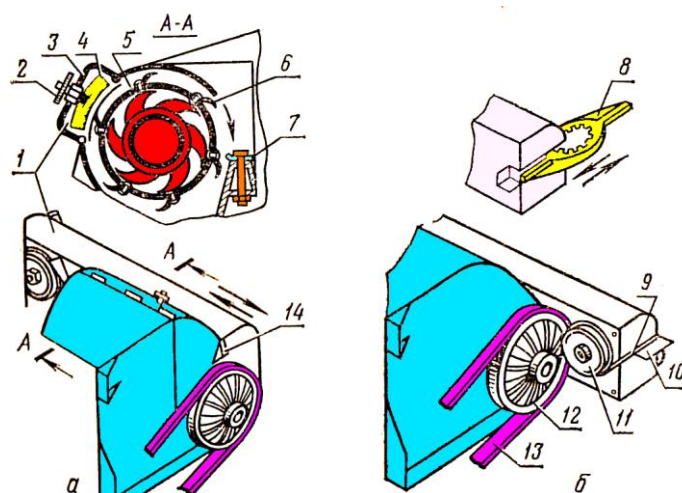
Схема заточки ножей: режущего барабана (*а*) и аппарата вторичного резания (*б*):
